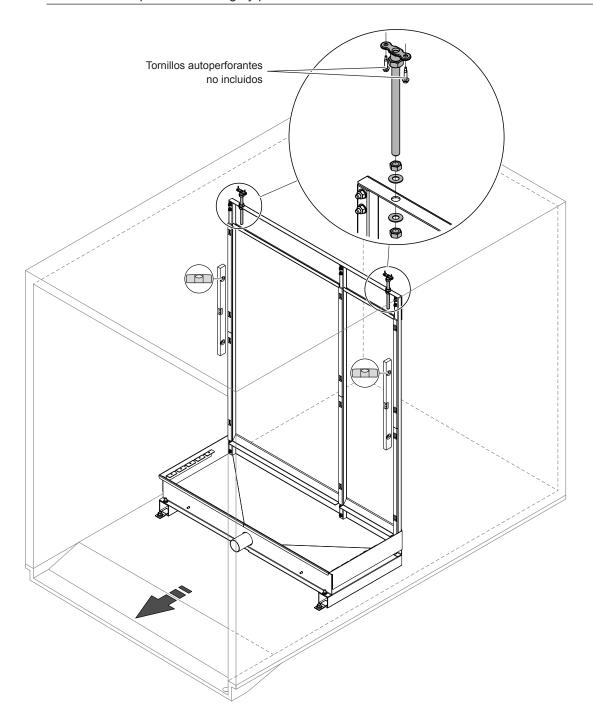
Fijación de la barra transversal al techo de la UTA / el conducto
